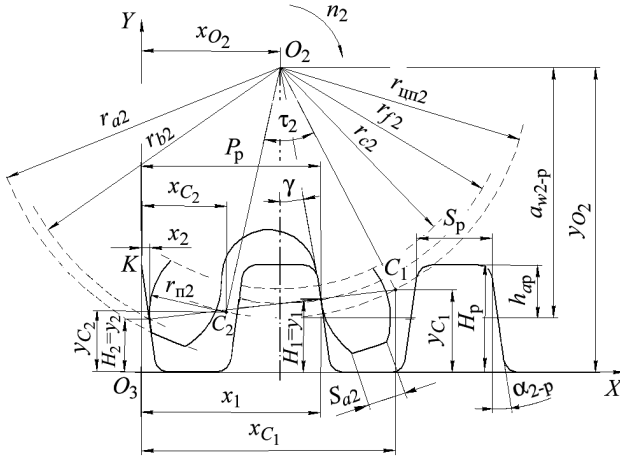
Расчетная схема к проектированию правых профилей зубьев зубчатого колеса для пары «зубчатое колесо – зубчатая рейка»
